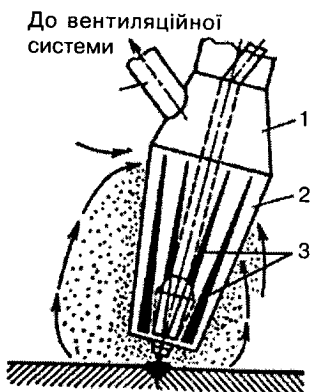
Конструкція малогабаритного відсмоктувача з клиноподібними щілинами конструкції НДІСТ:
